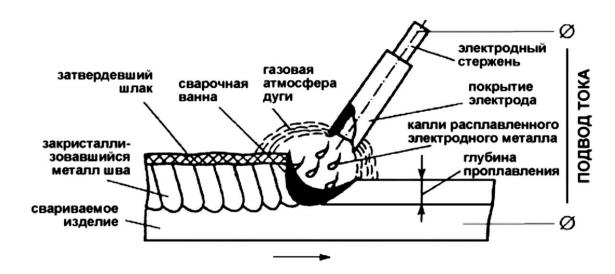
Схема дуговой сварки штучными электродами
